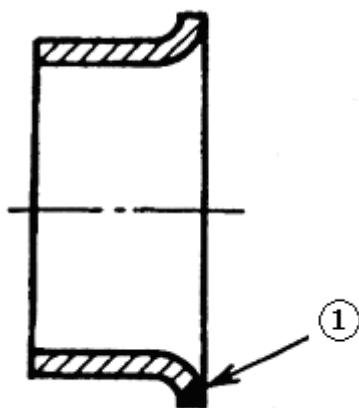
Дефект втулки упорной регулятора тормозной рычажной передачи, ремонтируемый сваркой
